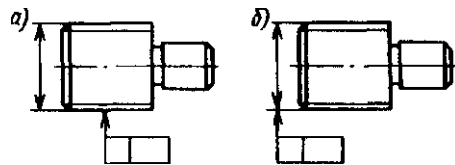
Нанесение допуска резьбы: а — боковой стороны резьбы; б — оси резьбы
